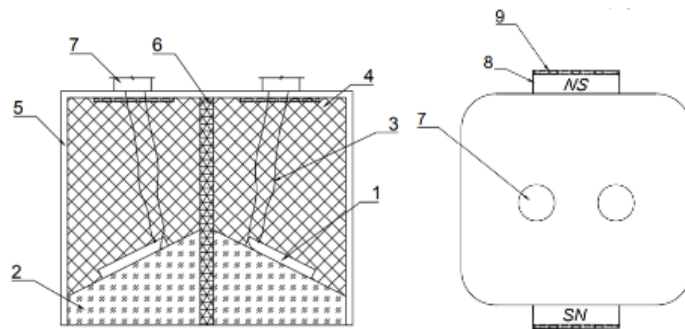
Конструкция ПЭП для разбраковки чугунов: 1 – пьезопластина; 2 – призма; 3 – проводники; 4 – демпфер; 5 – корпус; 6 – звукоизолирующая перегородка; 7 – разъем; 8 – магниты; 9 – магнитопровод
